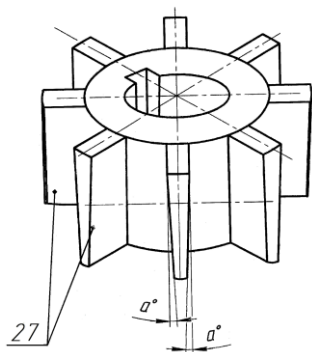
Пресс для брикетирования, общий вид формирующего колеса в аксонометрии: 27 – боковые поверхности пластинчатых зубьев
